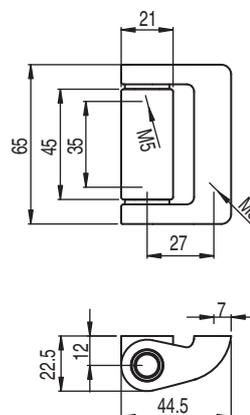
Dimensions de la charnière supplémentaire AC-H-S400-S en mm
